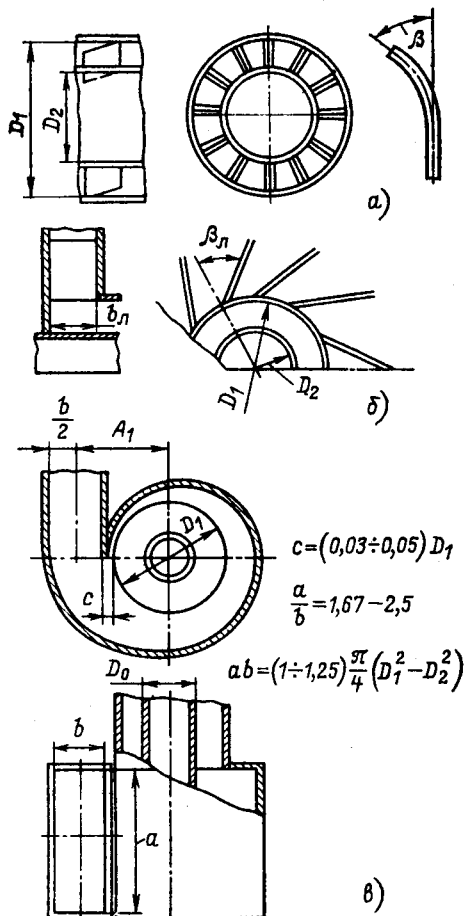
Конструктивные схемы закручивающих аппаратов:
